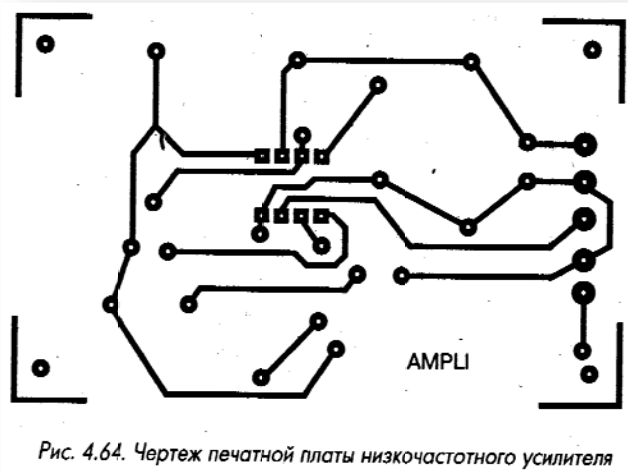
Чертеж печатной платы низкочастотного усилителя
